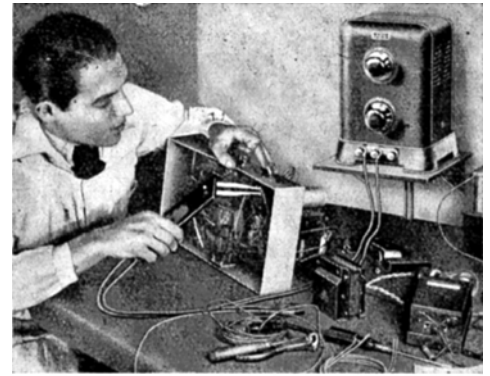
AEG-Kleinschweißzange mit zugehörigem Netzgerät im Gebrauch.
